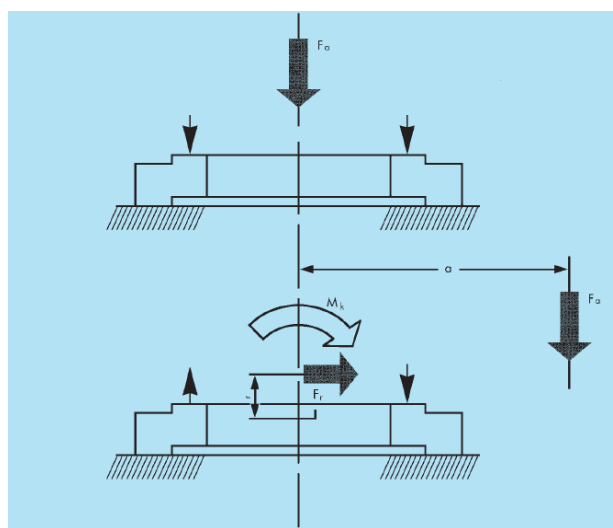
Cargas sobre el rodamiento ROTHE ERDE.
